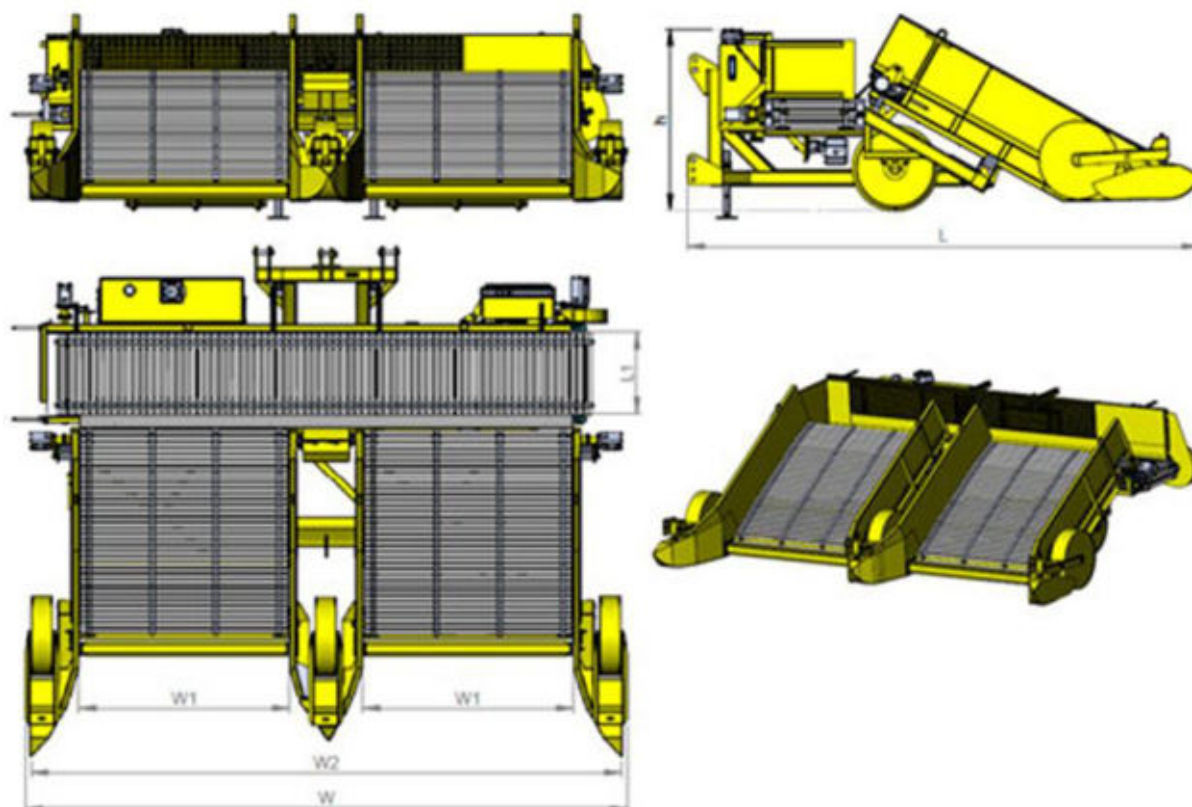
Основные размеры валкователя кускового торфа КА-4.0 Т
